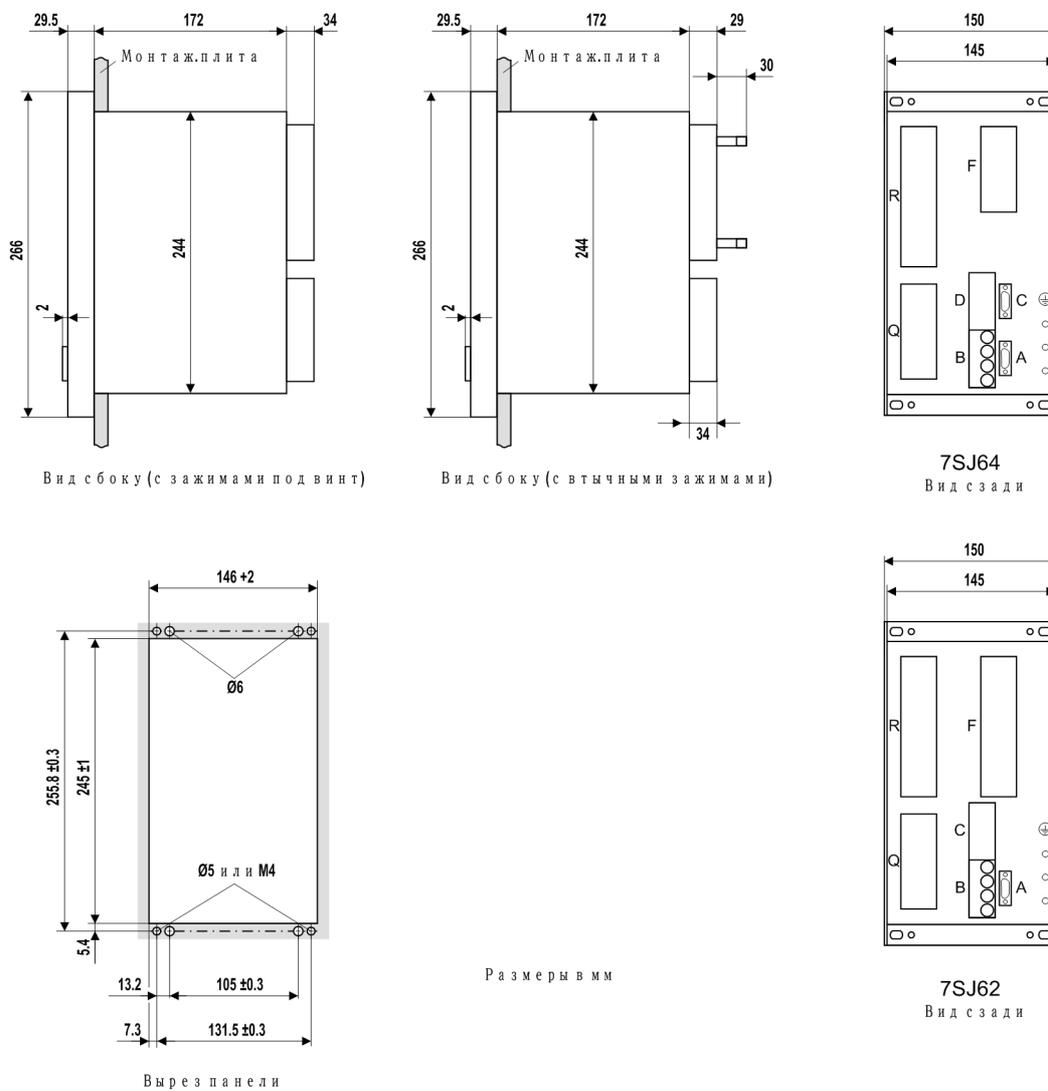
Размерный чертеж устройств 7SJ62 или 7SJ64 для утопленного монтажа на панели и в шкафу (размер корпуса  $\frac{1}{3}$ )
